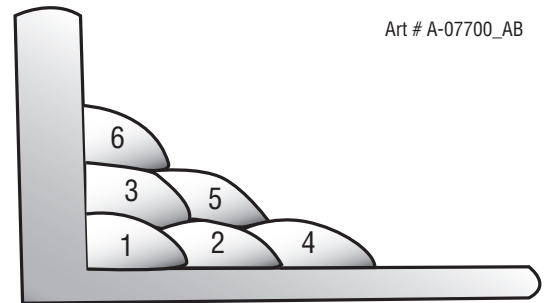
Plusieurs passages sur soudure d'angle HV
